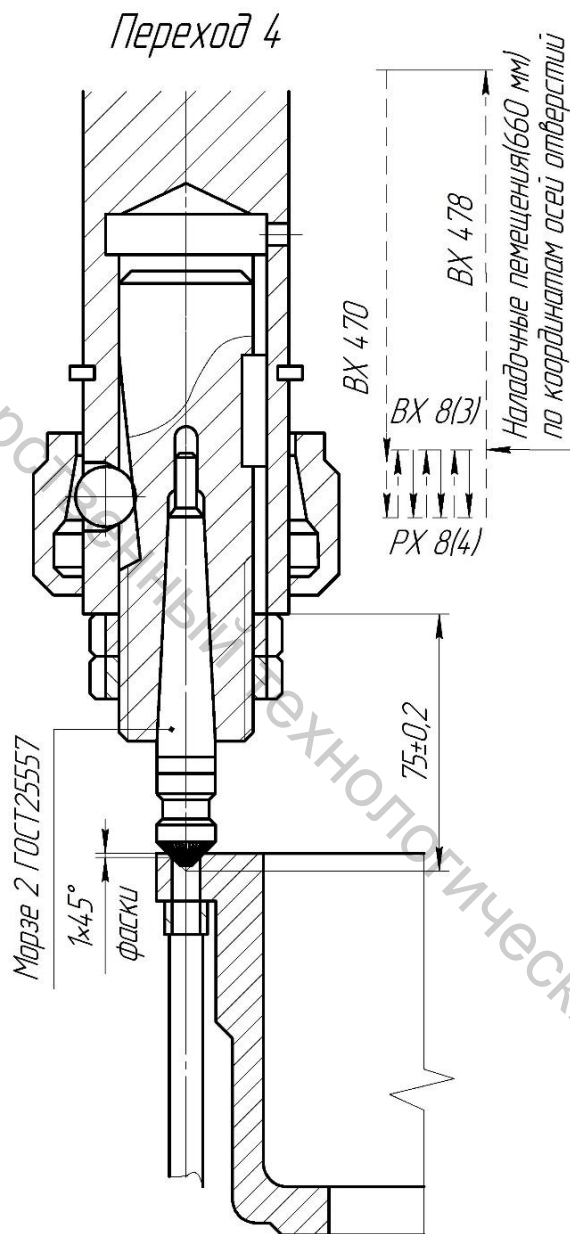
Схема наладки на переход 4 зенкования фасок
